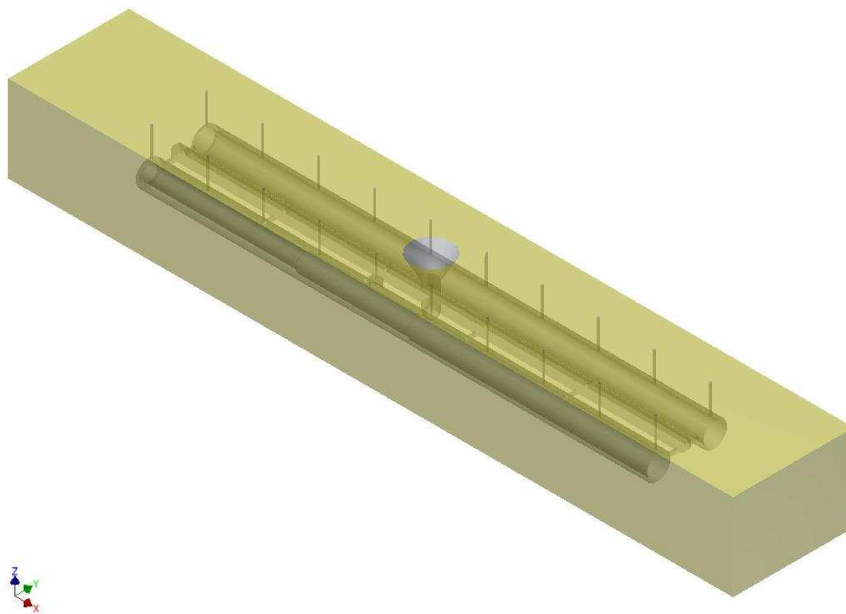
Modelo CAD de la arena de moldeo en la caja 1 de fundición.
